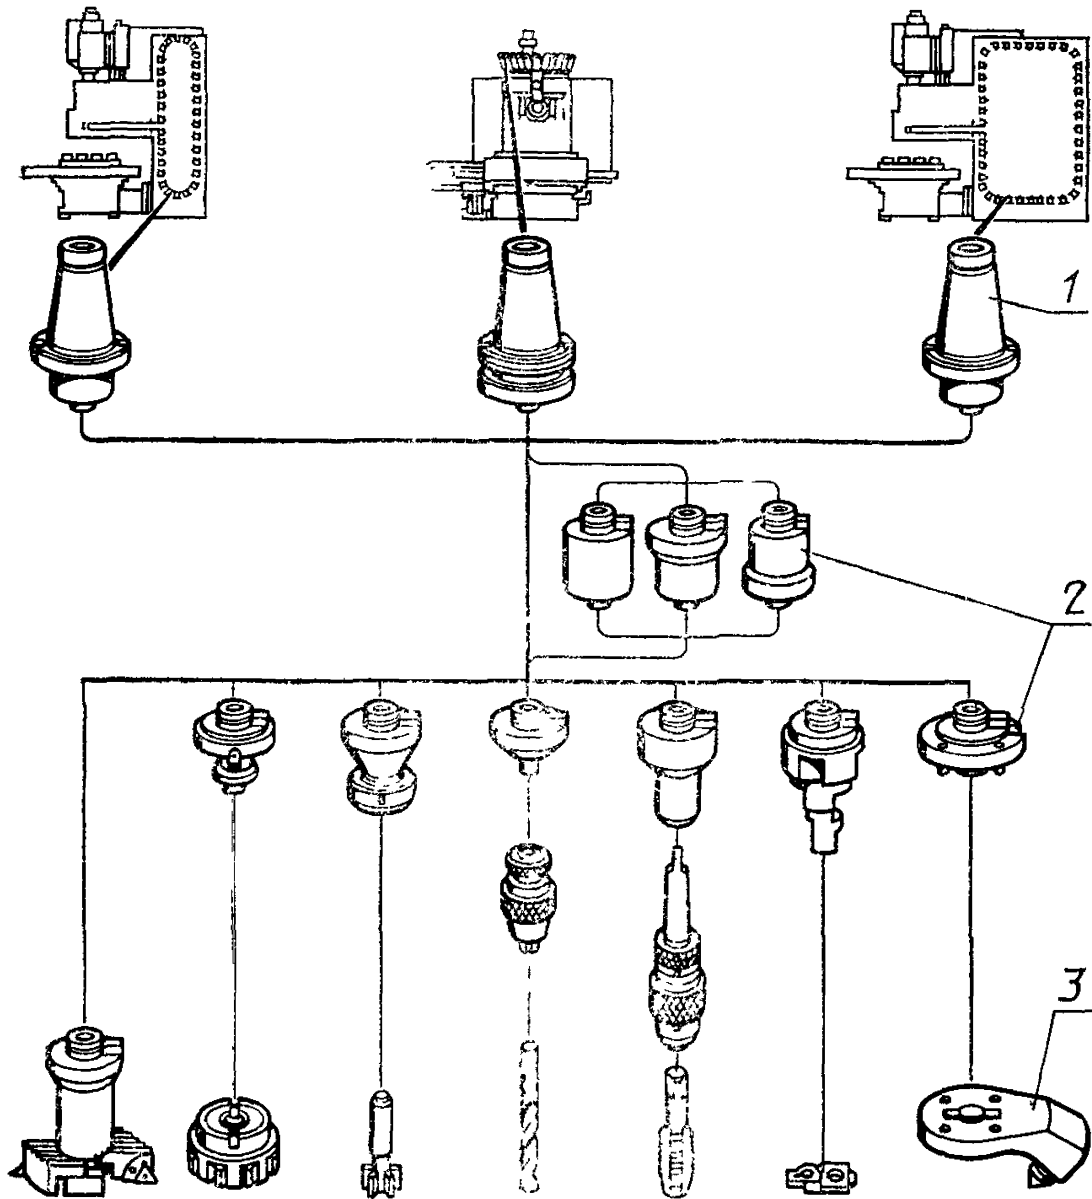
Пример блочно-модульного построения ЦКИ для станков фрезерной группы:
